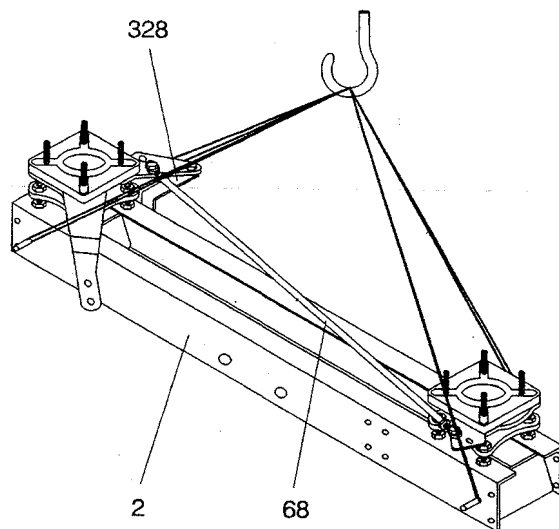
Установка разъединителя. Транспортировка рамы разъединителя (2) при монтаже на опорной конструкции
